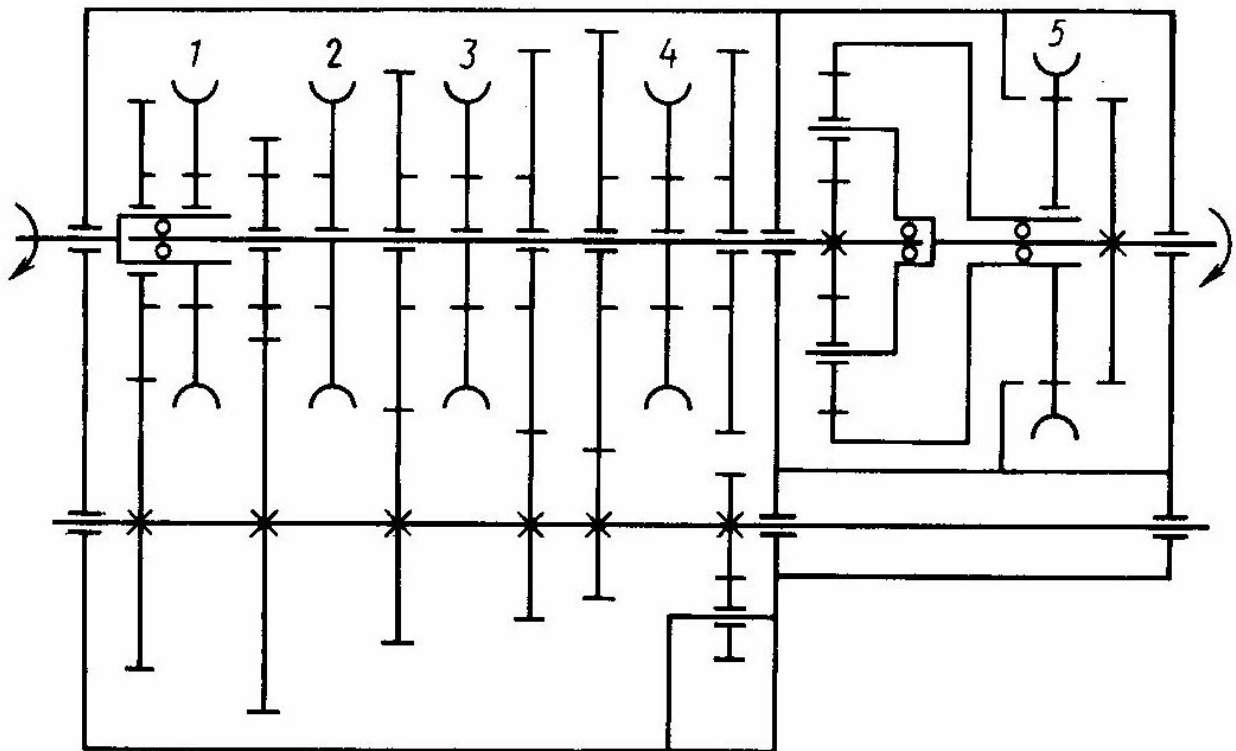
Кинематическая схема четырнадцатиступенчатой коробки передач
